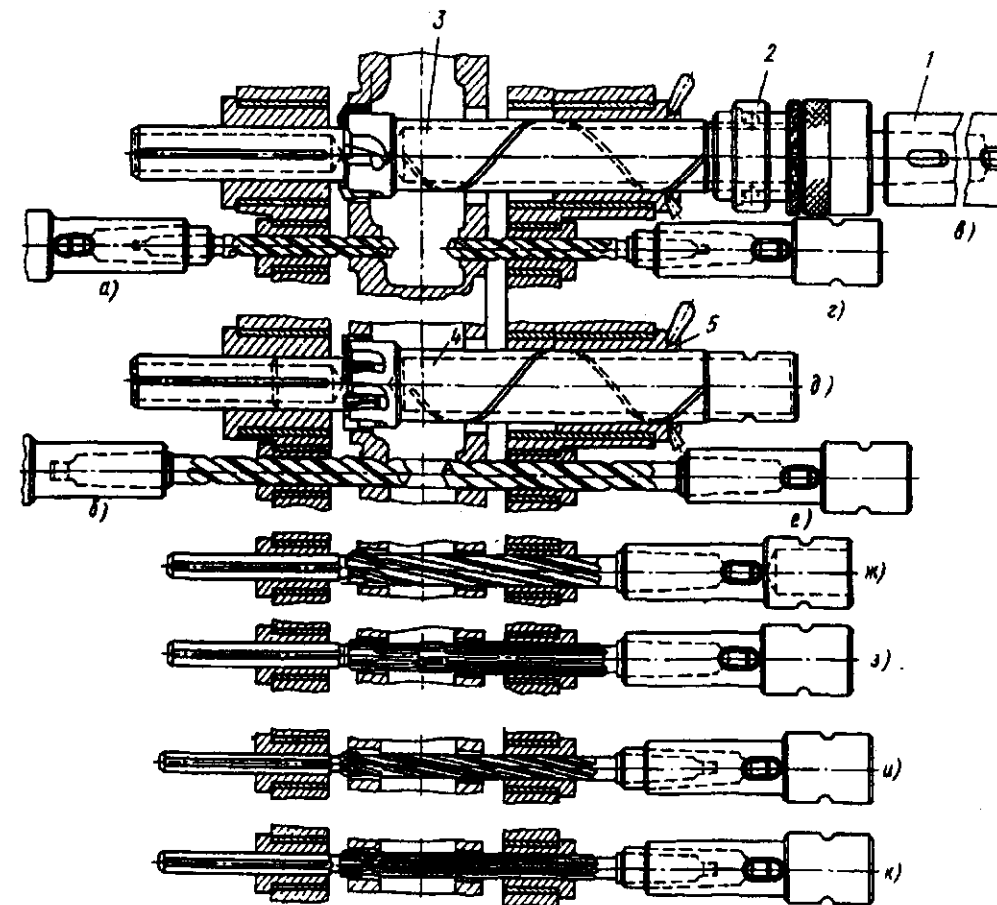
Схемы последовательной обработки корпусной детали в поворотном кондукторе
